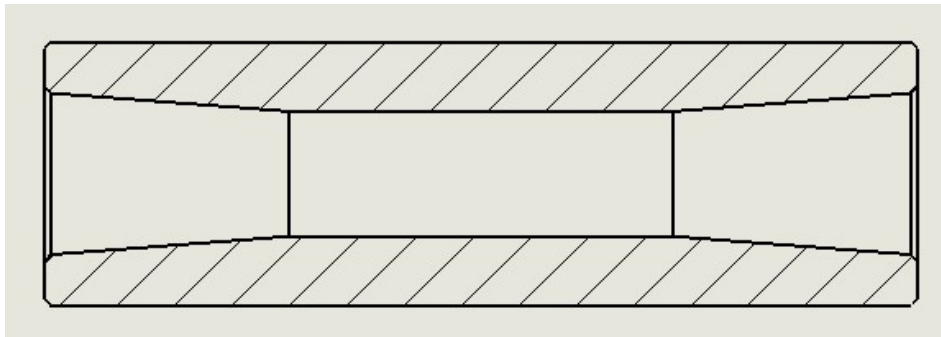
Exemplu de secțiune longitudinală prin bolt
